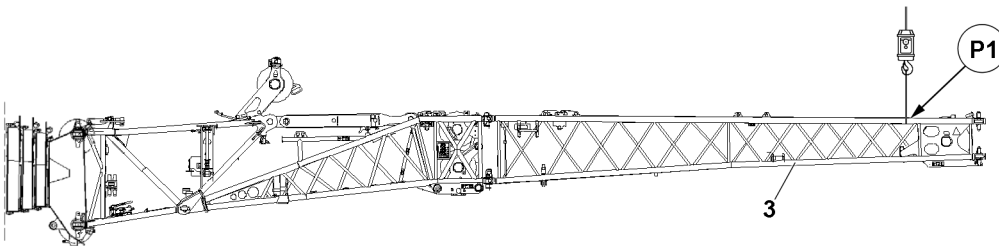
Converter o jib rebatível simples com o guindaste auxiliar
